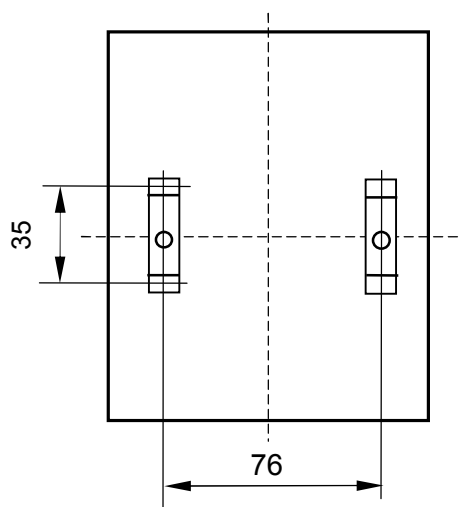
Габаритные и установочные размеры ИП с креплением на DIN – рейку (35 mm)
